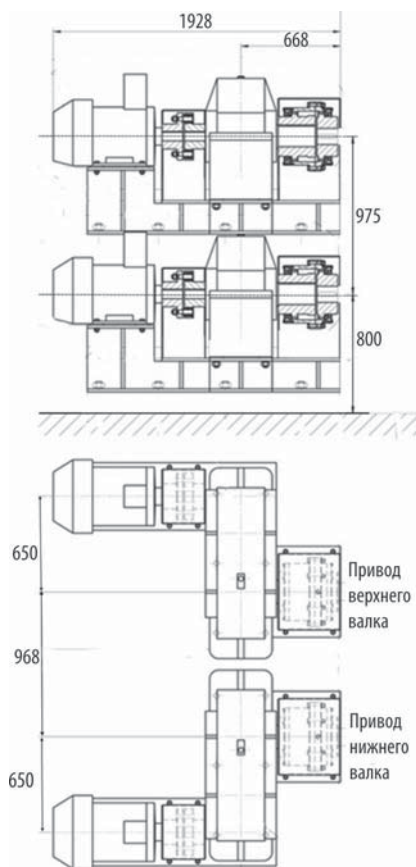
Расположение приводов верхнего левого и нижнего правого валков четырехвалковой дробилки до реинжиниринга
